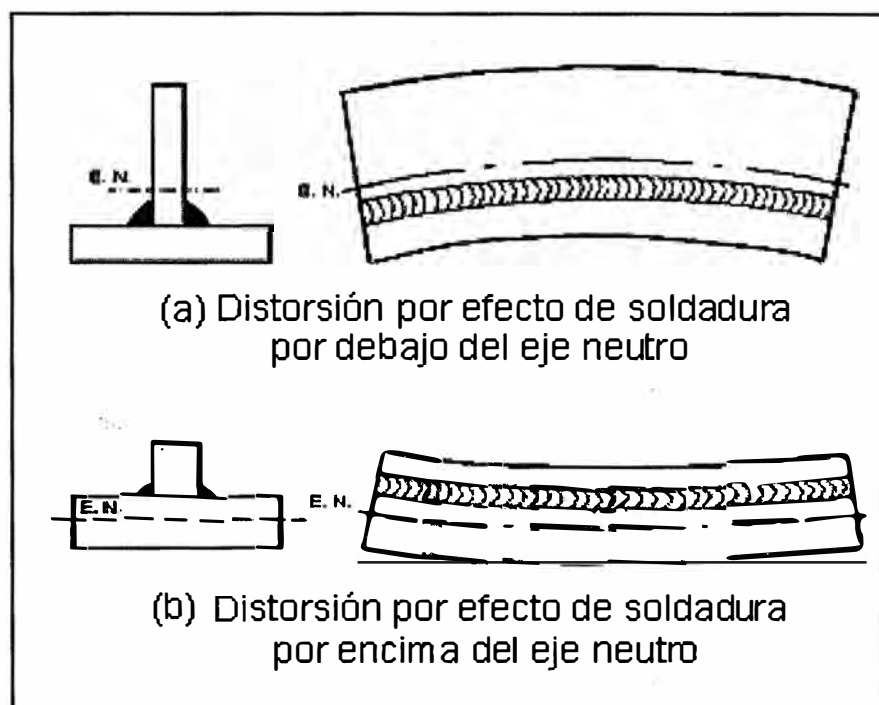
Distorsión en una soldadura en Angulo o distorsión longitudinal por flexión (2).
